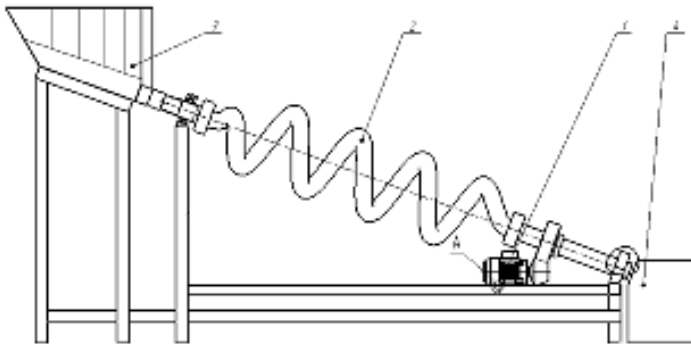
Предложенный смеситель кормов непрерывного типа
